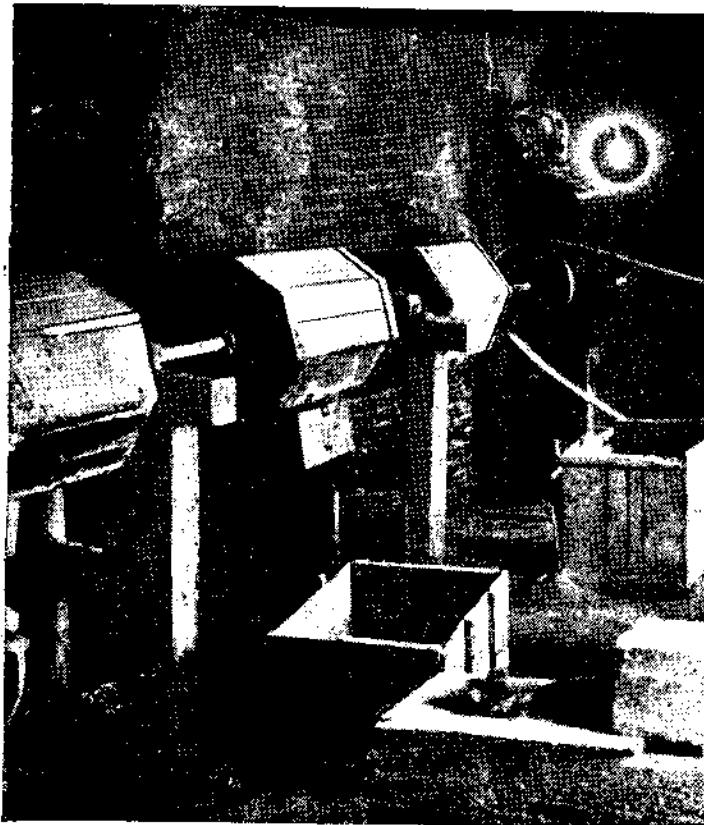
Галтовка и шлифовка пуговиц в барабанах.
